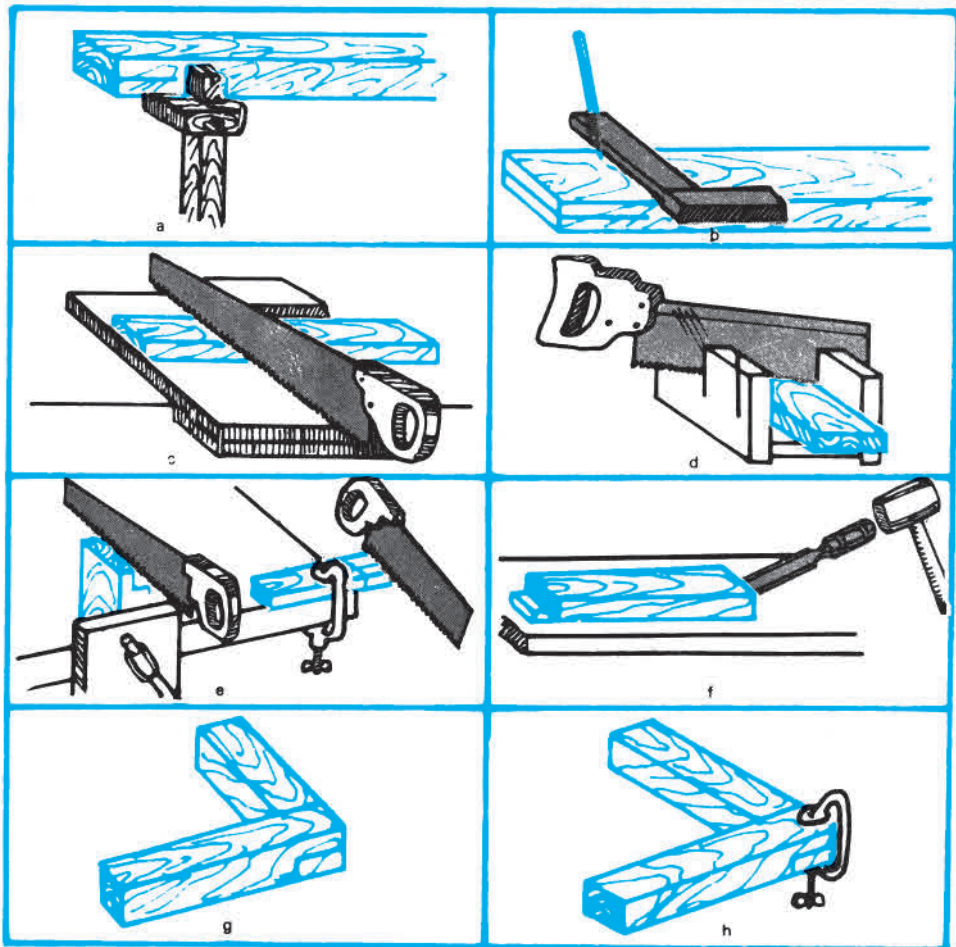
Ensamble a media madera a la cabeza; a) trazado con el gramil; b) trazado a 90° con escuadra y lápiz; c) corte con serrucho y sobrebanco; d) corte con serrucho de costilla y caja de corte inglete; e) corte del sobrante usando prensa de banco o presilla tipo C; f) corte del sobrante con trincha; g) ensamble de las piezas.
